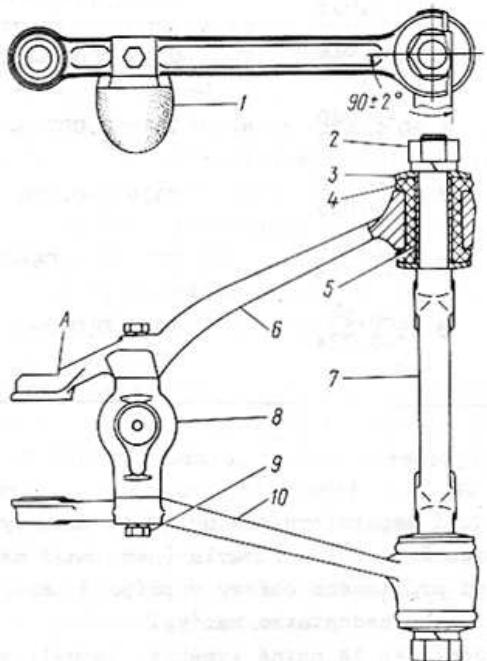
Přípravek 7823-5726 k výměně pryžových pouzder zavěšení předních kol a jeho použití:
